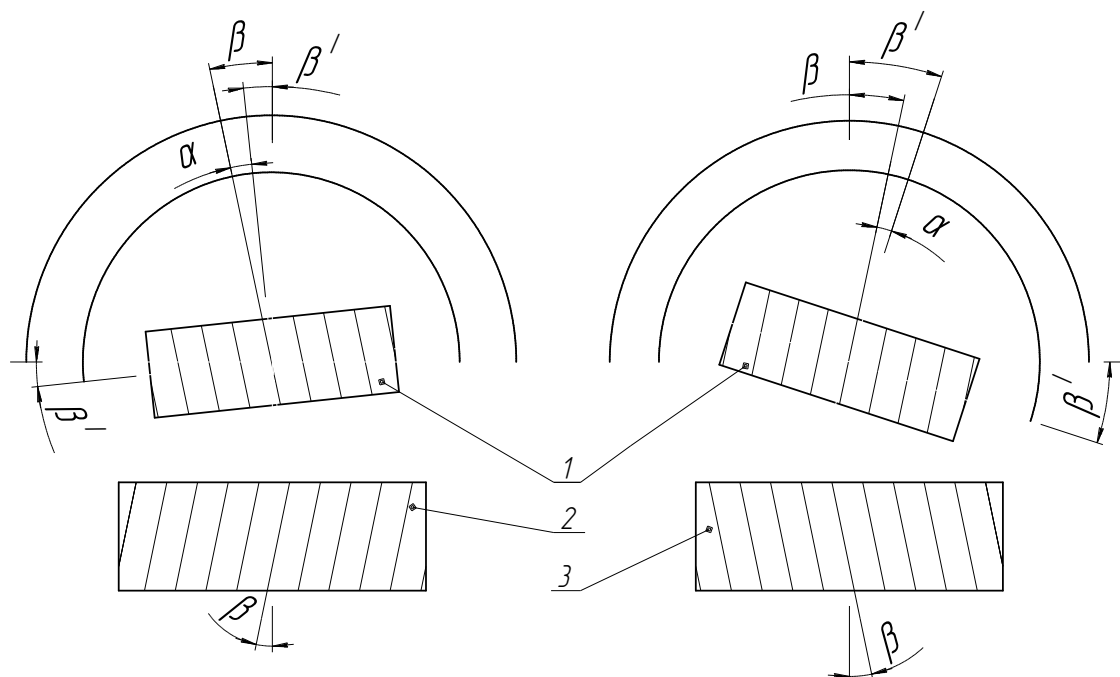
Установка червячной фрезы при зубонарезании цилиндрических косозубых колес: 1 – правозаходная фреза; 2 – правозаходное зубчатое колесо; 3 – левозаходное зубчатое колесо
